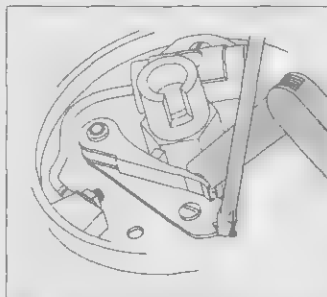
Регулировка контактов прерывателя с пазовой регулировкой
